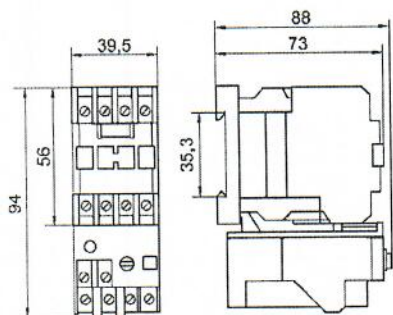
Пускатель нереверсивный ПМ12-010 10А.
